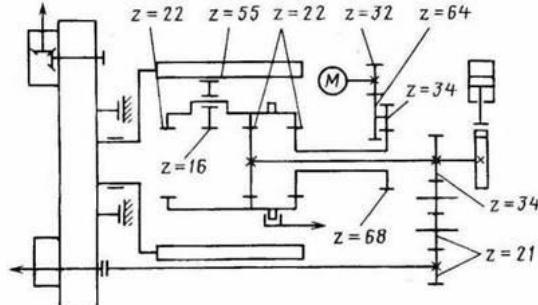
Кинематическая схема головки с приводом каждого инструмента
